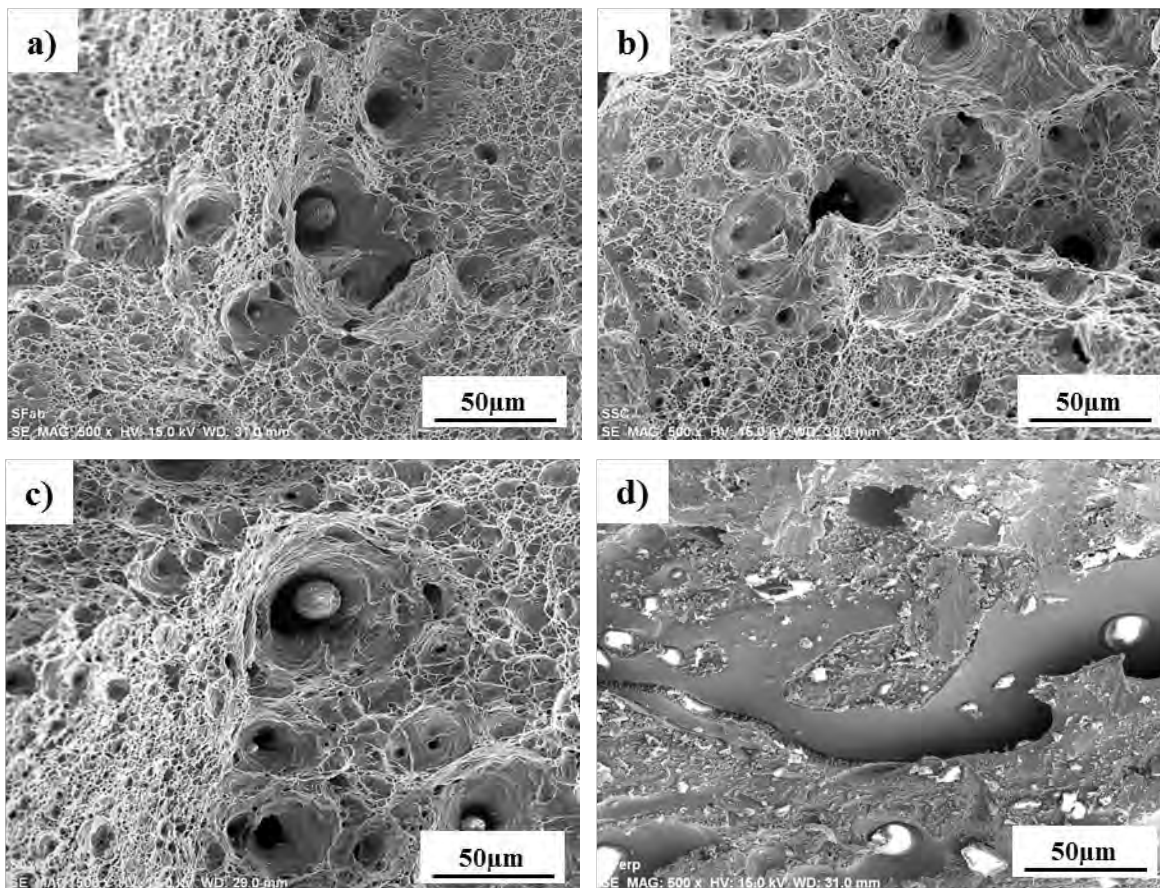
Imágenes obtenidas por MEB de las superficies de fractura de las probetas de tensión de las soldaduras del acero API X-60; a) de fábrica por SAW, b) sin CM por GMAW, c) con CMA por GMAW y d) con CMP por GMAW.
